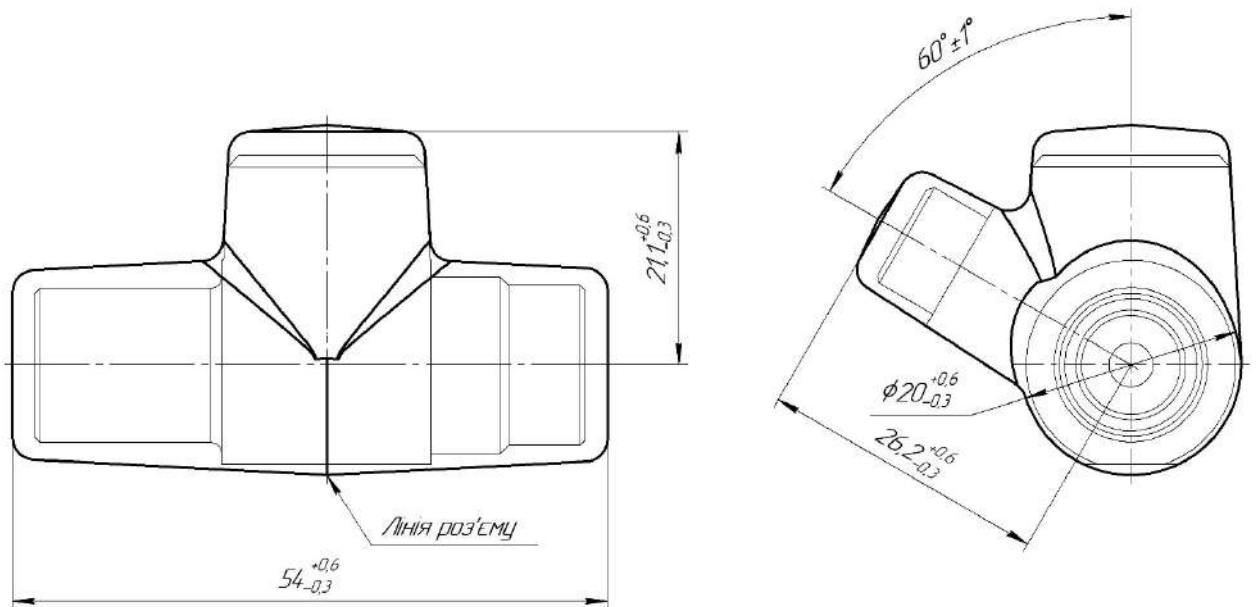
Заготовка корпусу, отримана способом гарячого штампування
